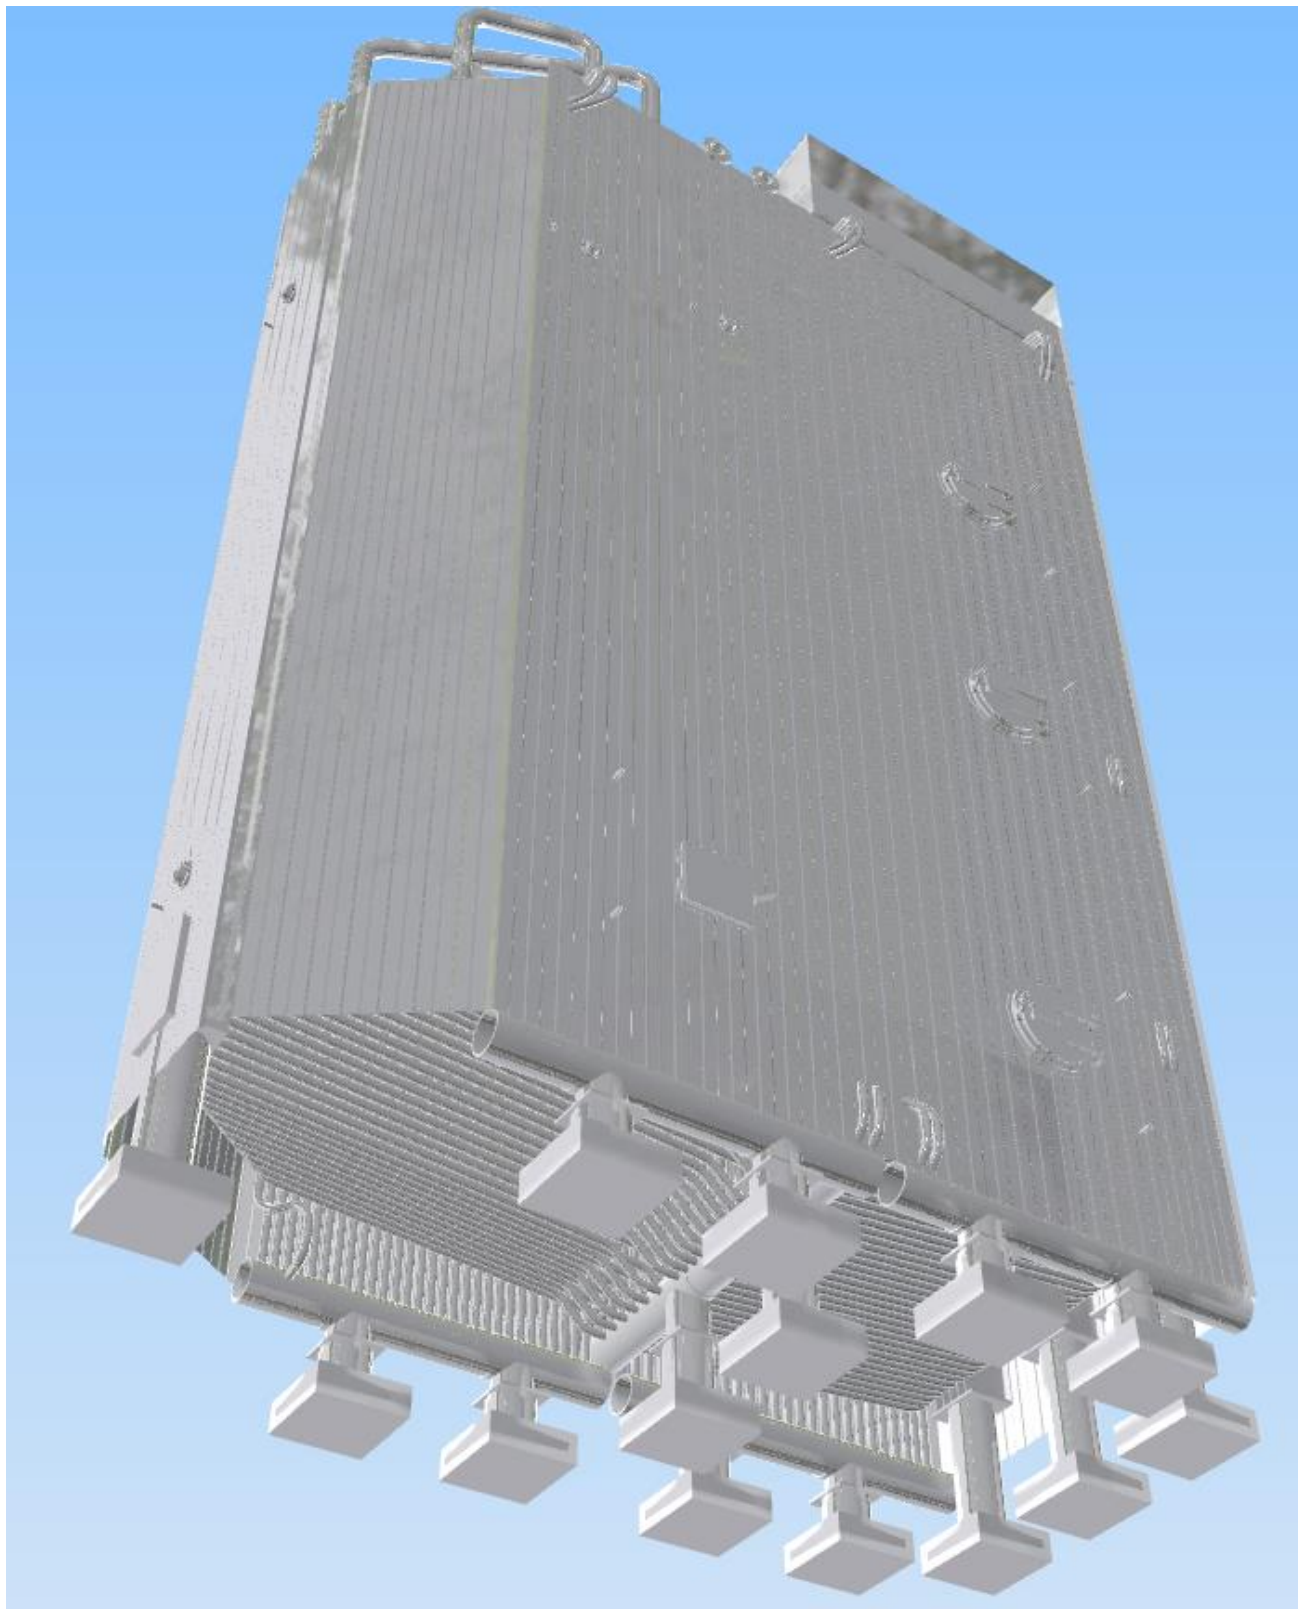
Общий вид котлоагрегата (вид снизу)
